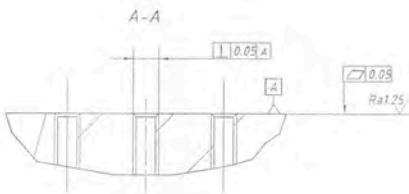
Разметка установочной площадки датчика ВД-30-3 (треугольное крепление)
